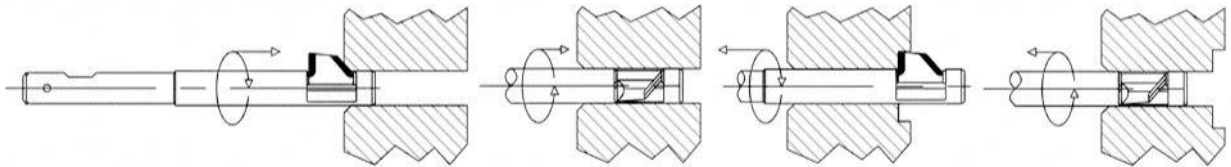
Принцип роботи інструменту Flipcut [2]
